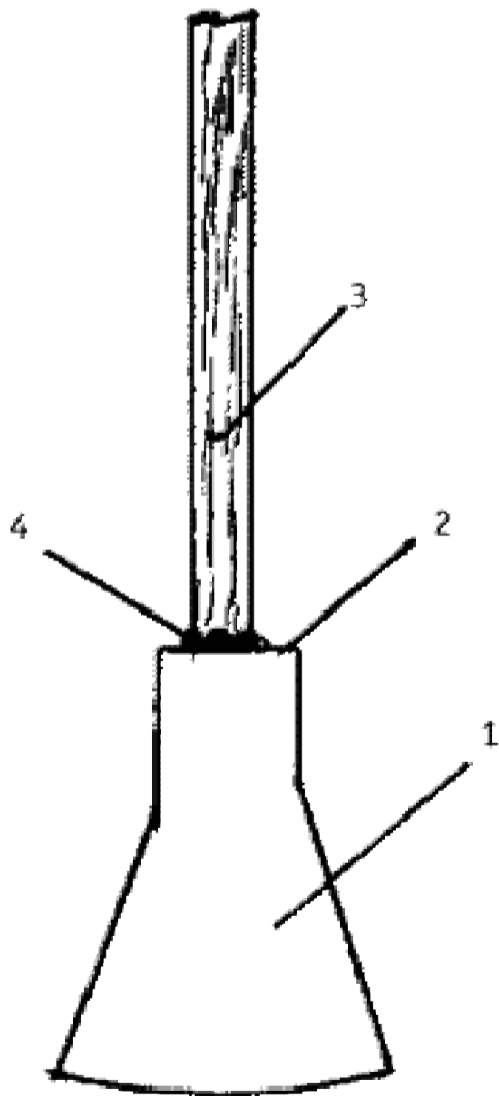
1 – лезвие, 2 – обух, 3 – труба, 4 – сварка
